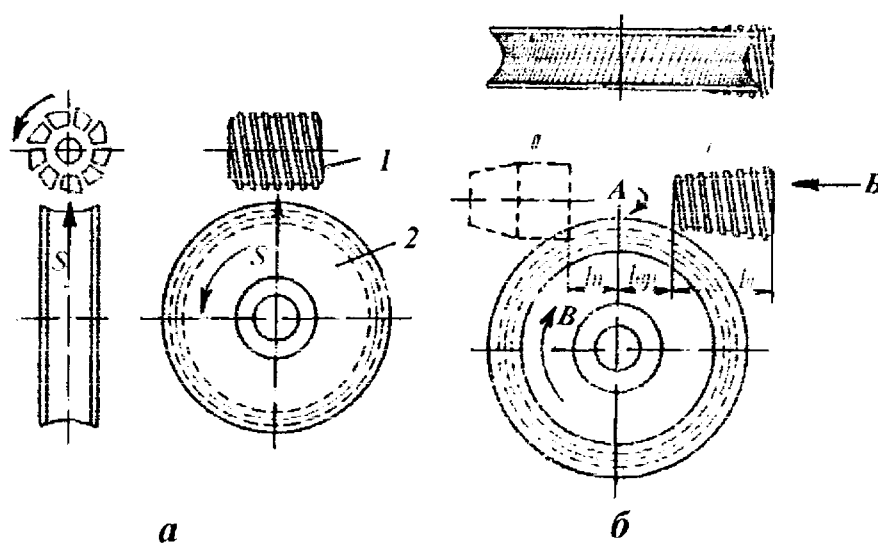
Схемы нарезания червячных зубчатых колес :
